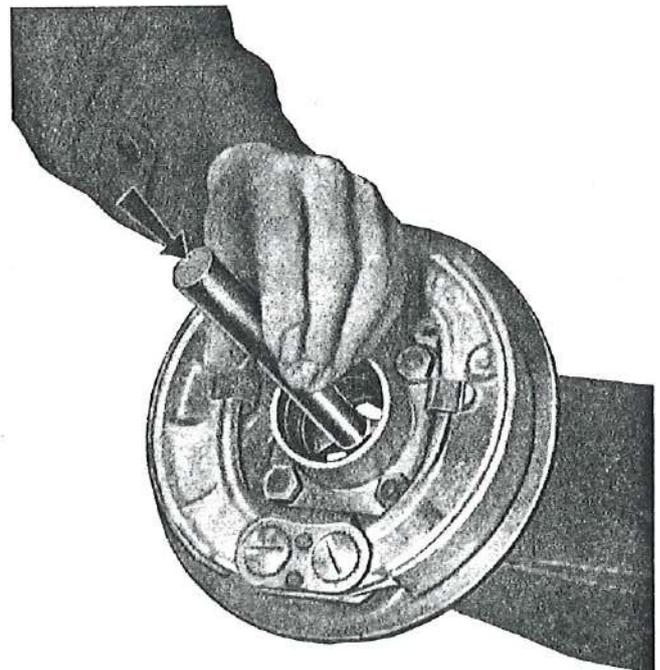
Desmontaje de los anillos exteriores de los rodamientos a rodillos interior y exterior, mediante el útil A. 66034.
